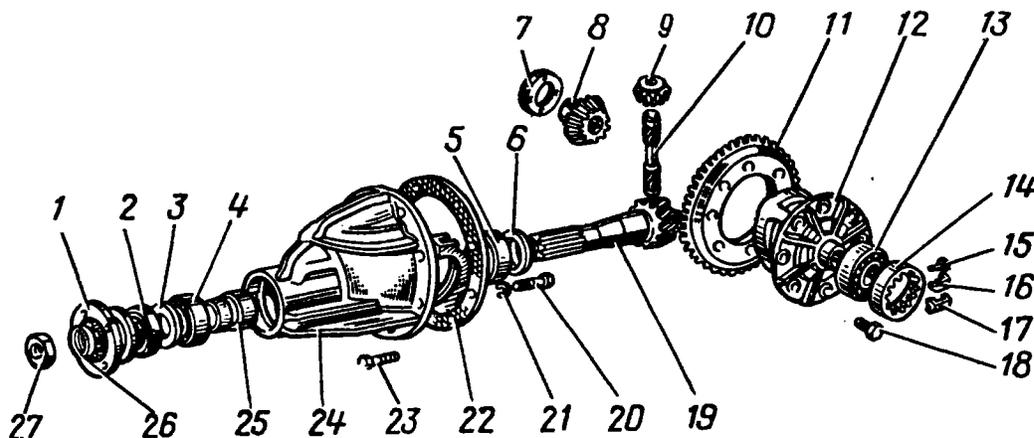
Детали редуктора заднего моста: 1 - фланец ведущей шестерни; 2 - сальник; 3 - маслоотражатель; 4 - передний подшипник; 5 - задний подшипник; 6 - регулировочное кольцо ведущей шестерни; 7 - опорная шайба шестерни полуоси; 8 - шестерня полуоси; 9 - сателлит; 10 - ось сателлитов; 11 - ведомая шестерня; 12 - коробка дифференциала; 13 - подшипник коробки дифференциала; 14 - регулировочная гайка; 15 - болт крепления стопорной пластины; 16 - стопорная пластина; 17 - стопорная пластина; 18 - болт крепления ведомой шестерни к коробке дифференциала; 19 - ведущая шестерня; 20 - болт крепления крышки; 21 - пружинная шайба; 22 - прокладка; 23 - болт крепления редуктора к балке заднего моста; 24 - картер редуктора; 25 - распорная втулка; 26 - плоская шайба; 27 - гайка крепления фланца ведущей шестерни
